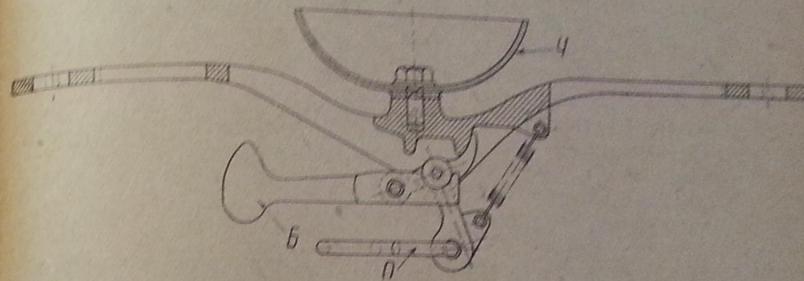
Сигнальный звонок кондуктора: *Ч* — чашка звонка, *Б* — боек, *О* — отверстие для веревки.
